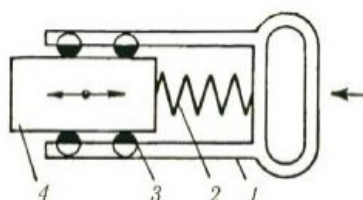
Схема віброізольованого держака: 1 – держак; 2 – пружний елемент; 3 – підшипник; 4 - корпус
